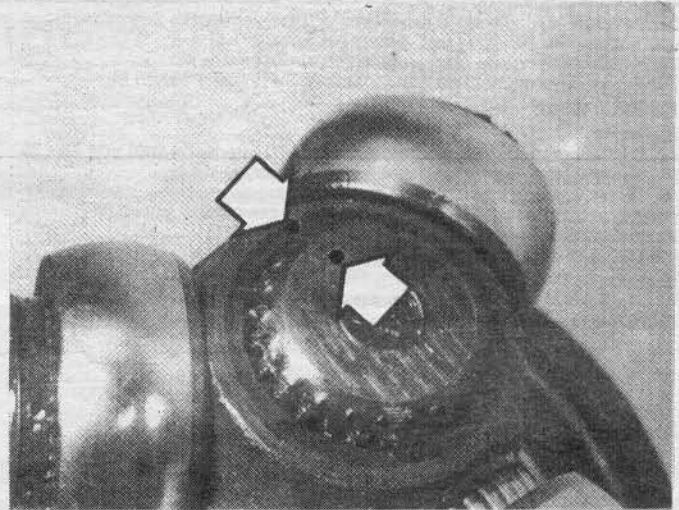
Метки взаимного положения (стрелки) крестовины и приводного вала.
